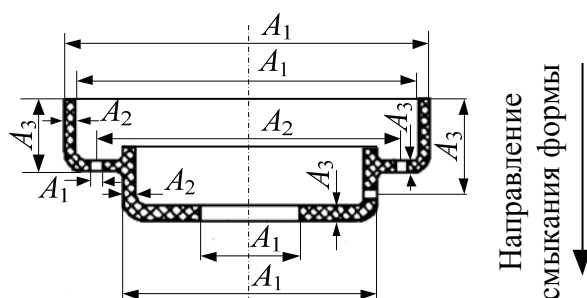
Типы размеров изделий из пластмасс, изготавливаемых в замкнутых формах прессованием и литьем под давлением
